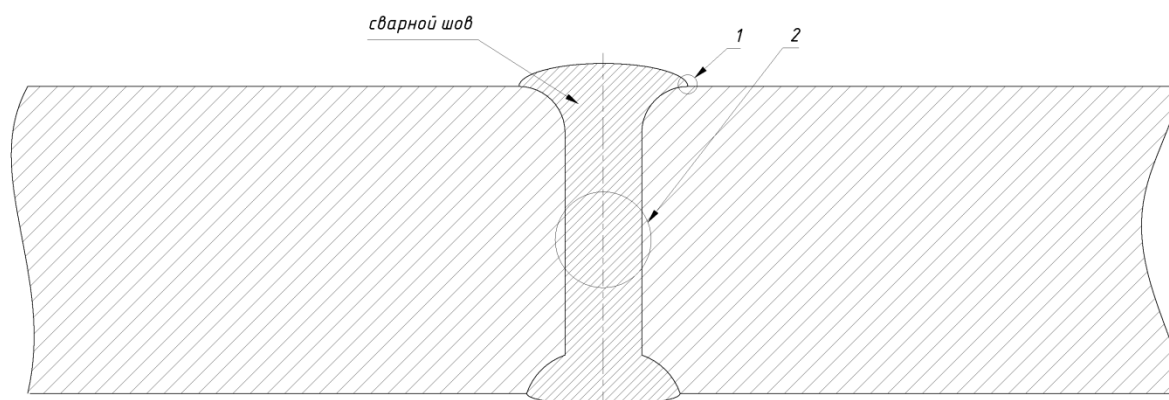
Сварной шов в толстостенной конструкции.
